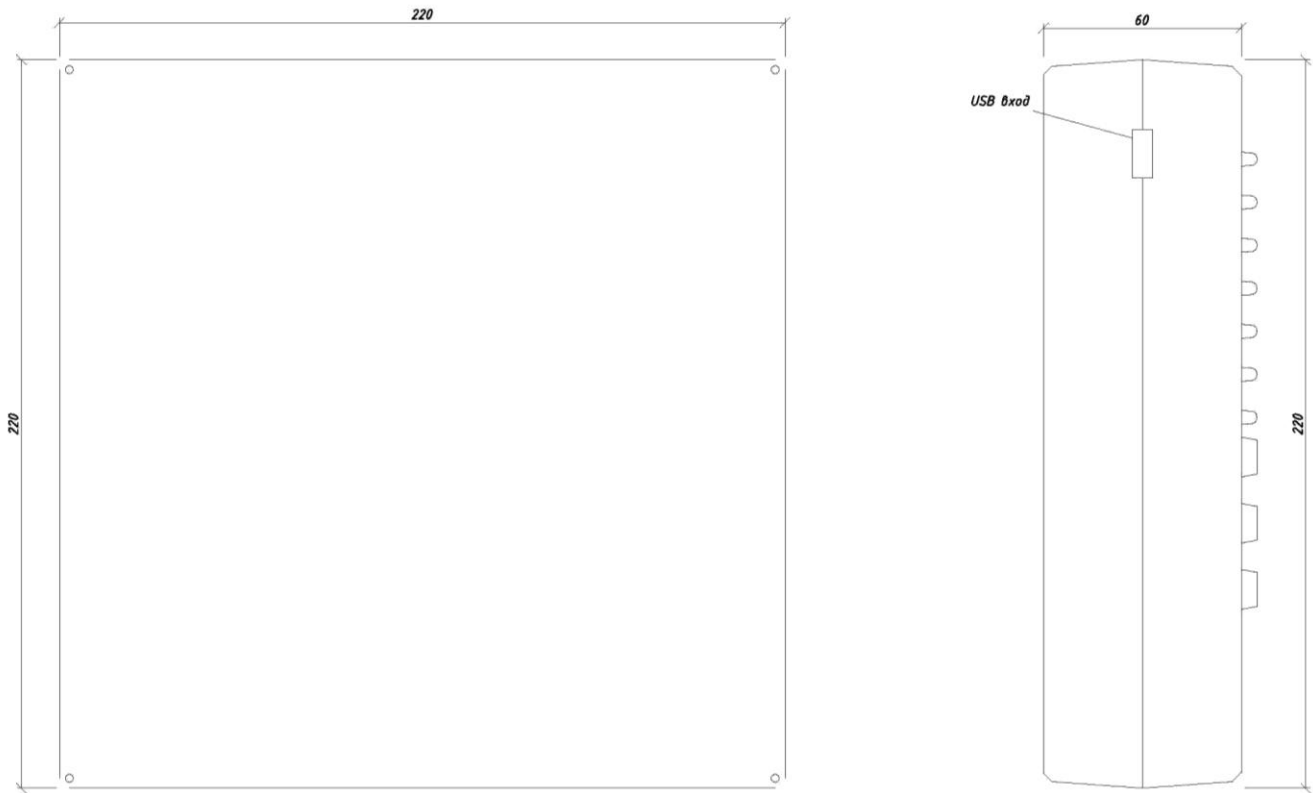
Габаритные и установочные размеры блока индикации «БАС-12Д»
